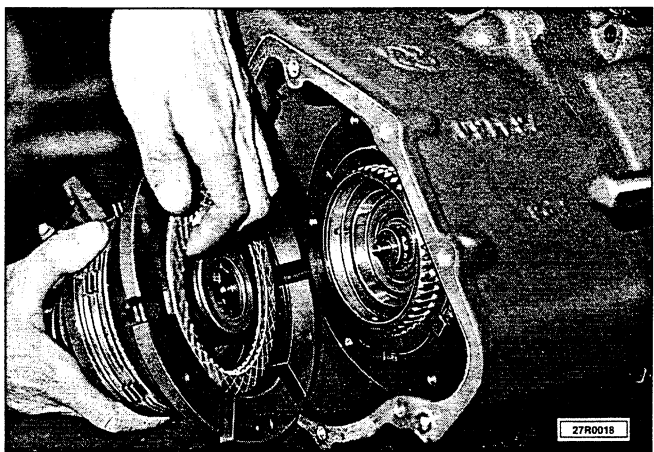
Desmontaje de los discos embrague de acoplamiento hidráulico;
